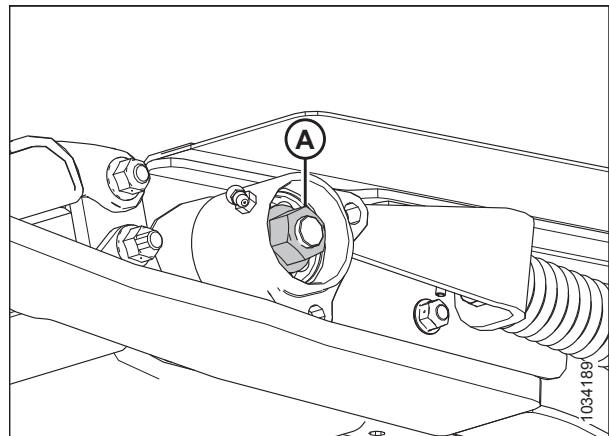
Rodamiento de rodillo tensor: lado izquierdo
